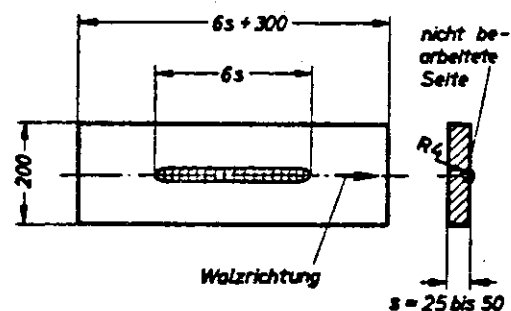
Probe für den Aufschweißbiegeversuch
